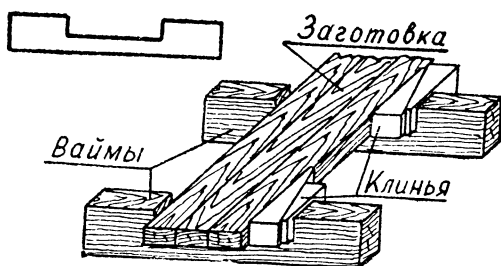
Запрессовка заготовок в ваймах — для склеивания.
